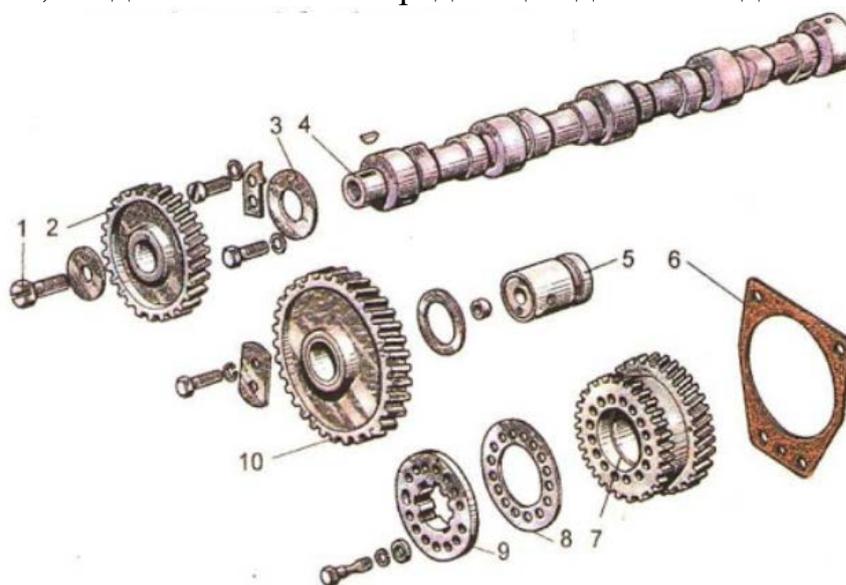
ГРМ двигателя Д-240: 1 – болт; 2 – шестерня привода распределительного вала; 3 – шайба; 4 – распределительный вал; 5 – палец; 6 – прокладка; 7 – шестерня привода топливного насоса высокого давления; 8 – упорное кольцо; 9 – фланец
